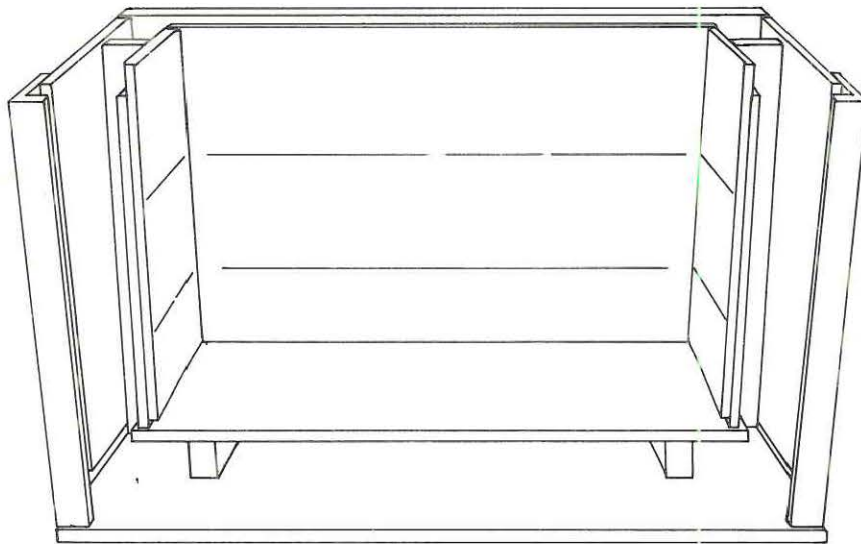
Vista frontal del fermentador sin las caras removibles.
